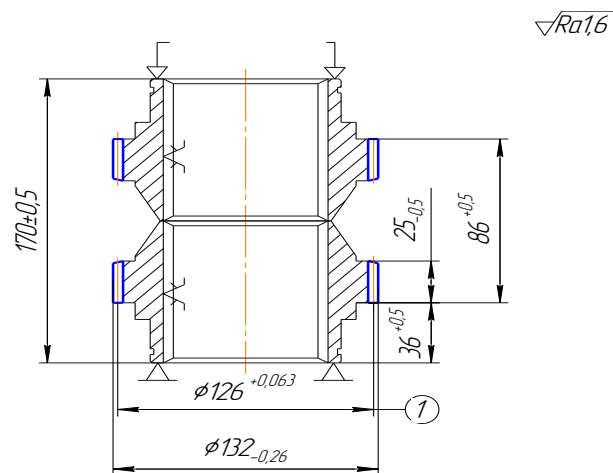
Ескіз на зубофрезерних операцію
